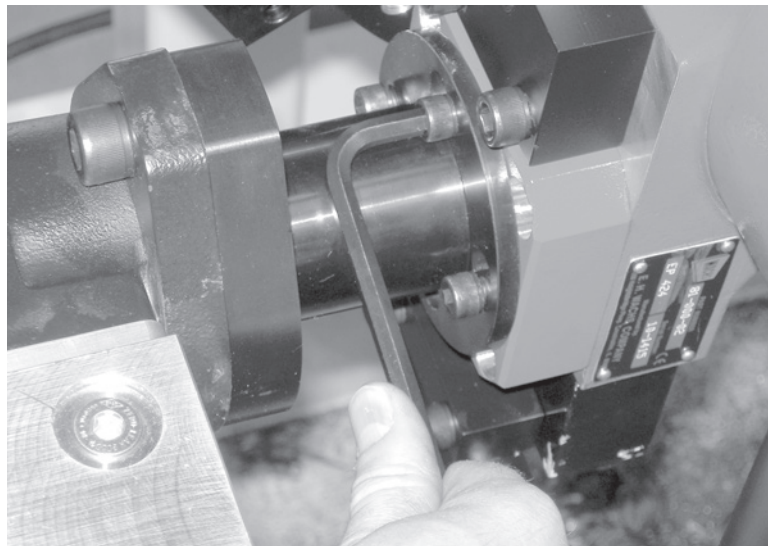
Ruotare la flangia per inserire le viti nelle rispettive sedi, quindi serrare le viti.
